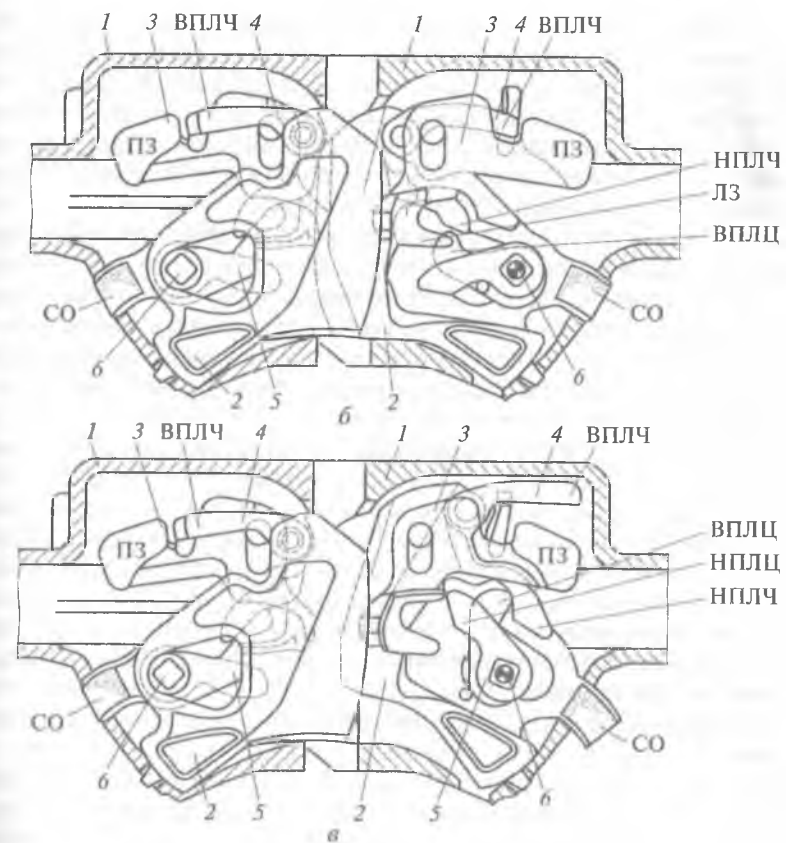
Установка элементов сцепного механизма в корпус автосцепки
